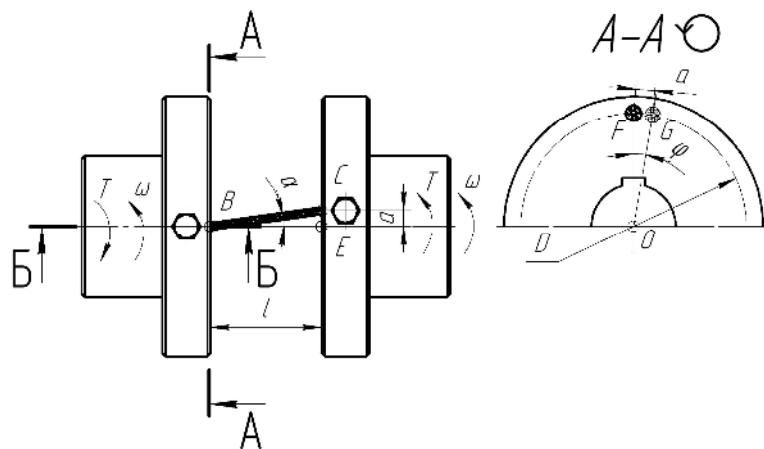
Розрахункова схема муфти з осью паралельною установкою канатів прямолінійної форми
